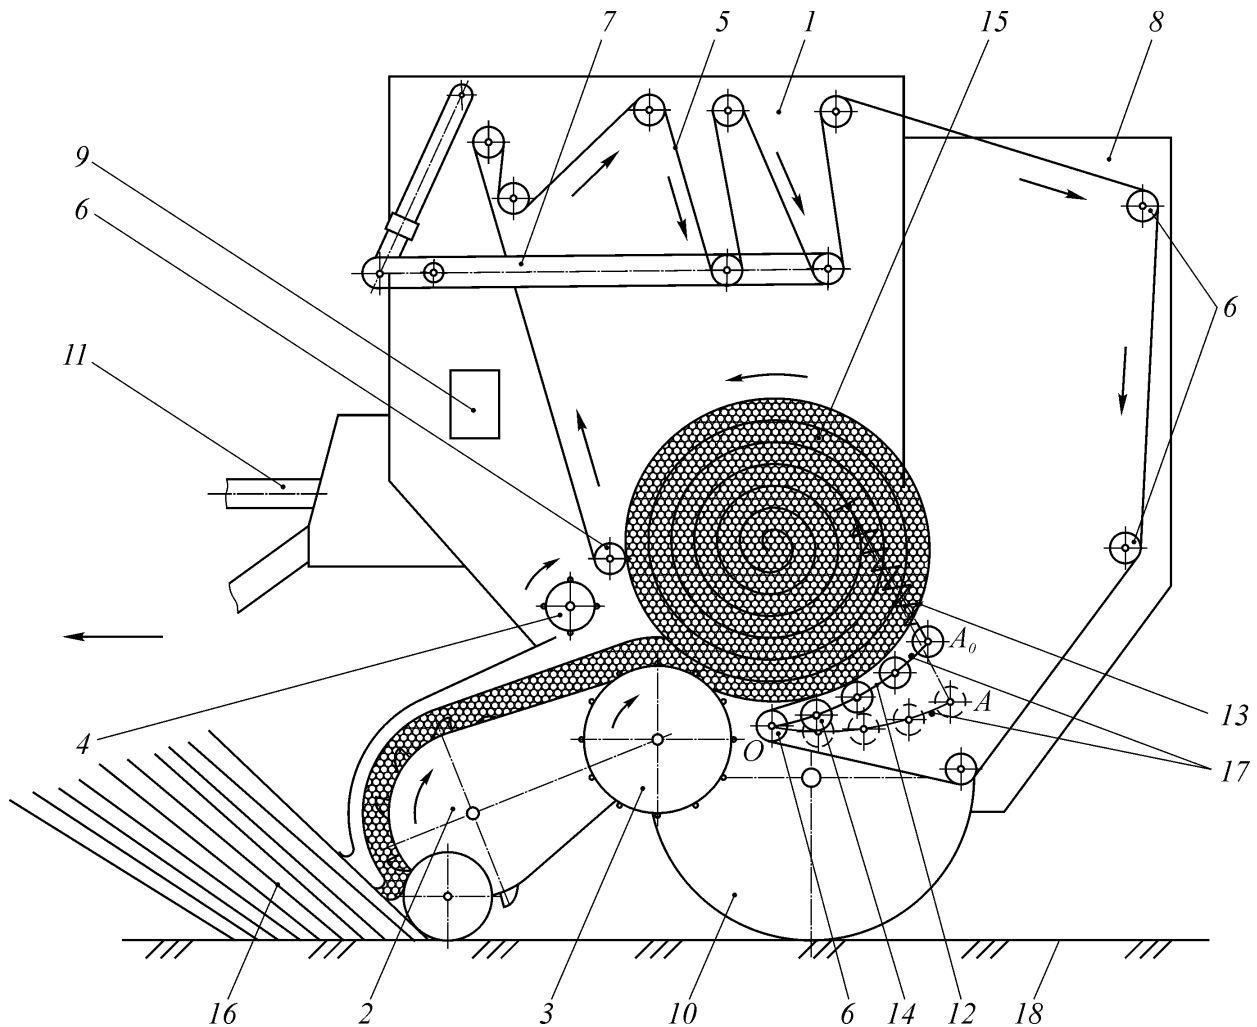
Схема рулонного прес-підбирача енергетичної верби: 1 – рама; 2 – різальний апарат; 3 – барабан; 4 – відбійний валик; 5 – нескінченні паси; 6, 14 – валики; 7 – натяжний пристрій; 8 – клапан вивантаження; 9 – обмотувальний апарат; 10 – ходова частина; 11 – механізм приводу; 12 – підпружинена рамка; 13 – пружини розтягу; 15 – рулон; 16 – енергетична верба; 17 – обмежувачі ходу; 18 – поверхня поля
